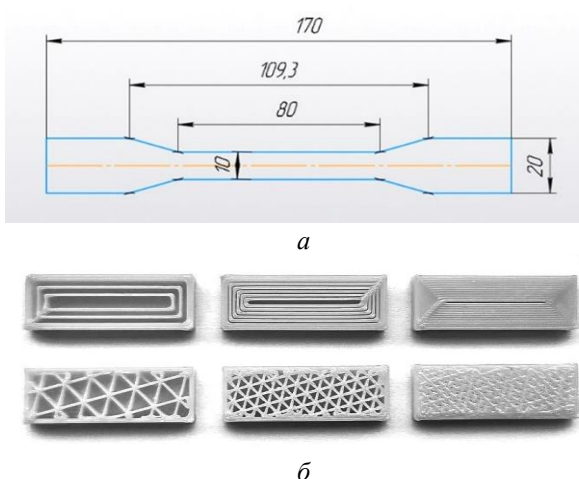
Параметры образцов для испытаний, где: а – чертеж образца с размерами, б – различная плотность заполнения 33%, 66% и 99% для концентрического типа структуры (сверху) и треугольного типа структуры (снизу)
